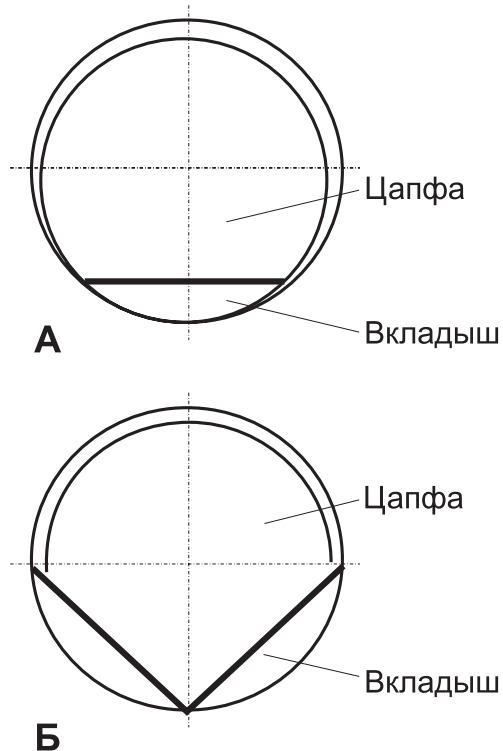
Конструкции периферийного подшипника долота с одним (А) и двумя вкладышами (Б)
